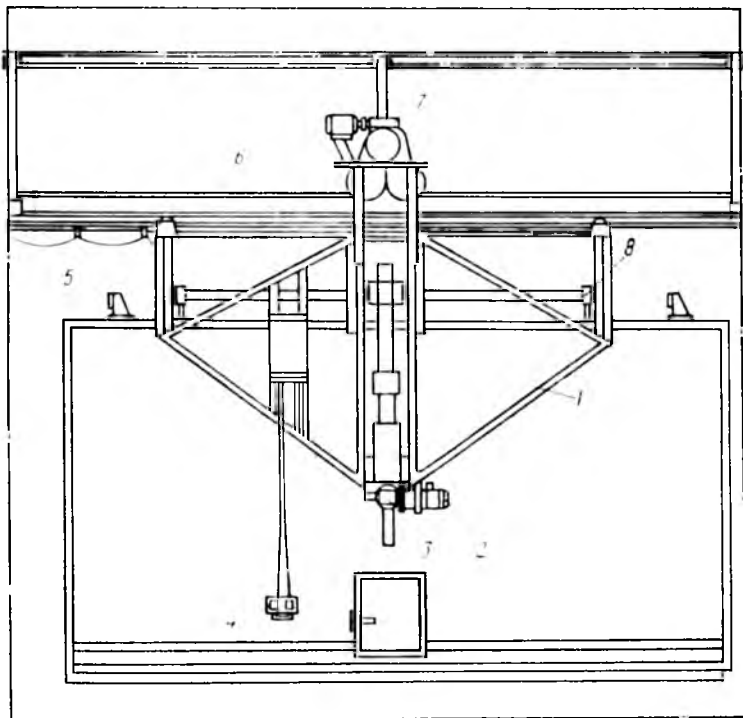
Подъемно-сдвижное устройство дверей сушилки «Валмет»:
